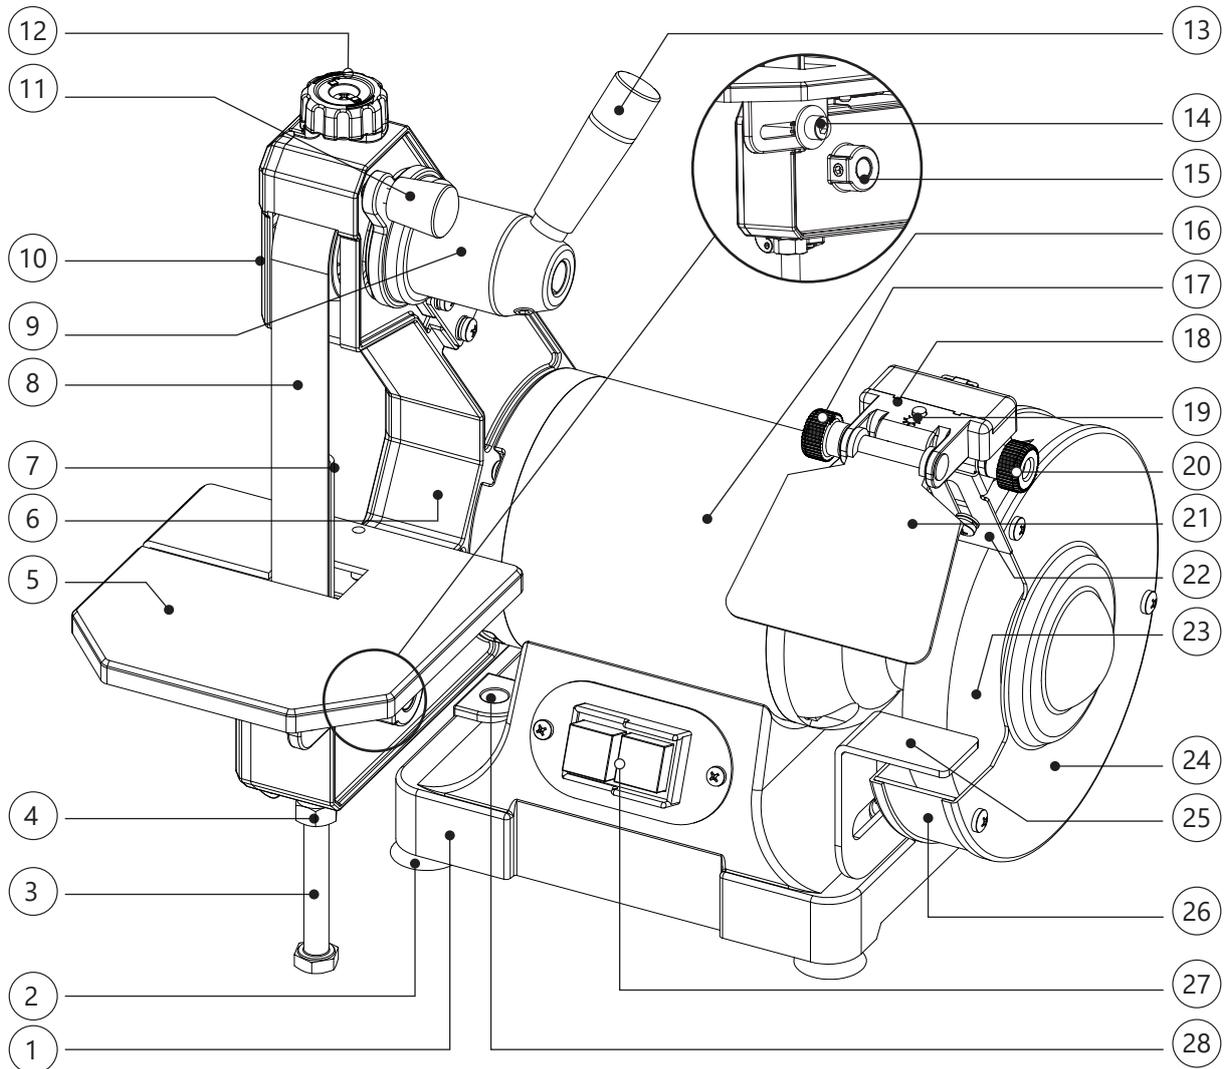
Основные элементы станка BELMASH MBG-150/25L.
